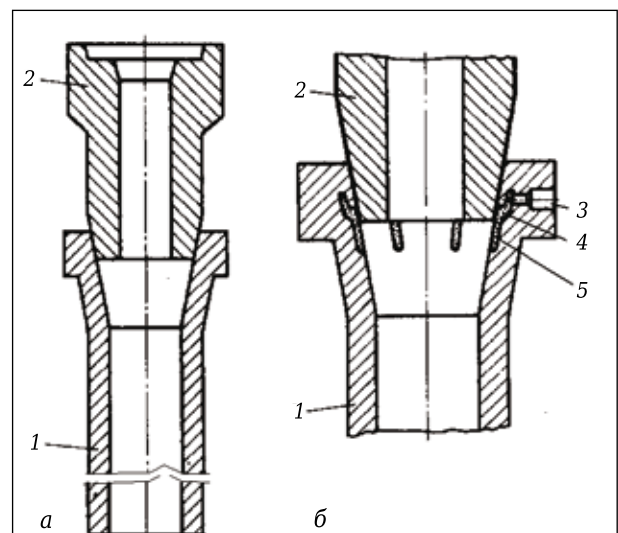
Установка защитной трубы сталеразливочного ковша: а — без подачи аргона; б — с подачей аргона; 1 — защитная труба; 2 — разливочный стакан; 3 — отверстие для подачи аргона; 4 — уплотнительное устройство; 5 — пазы для подачи аргона
